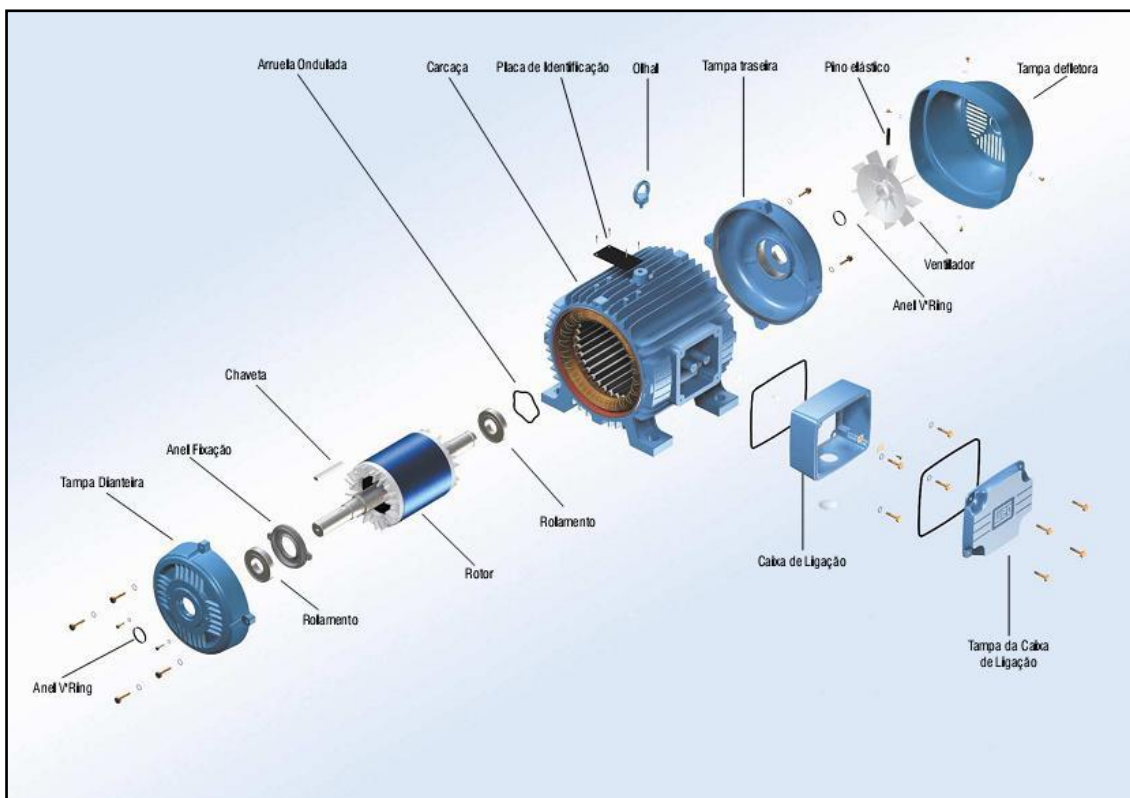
Partes constituintes de um motor de indução trifásico fabricado pela WEG.
